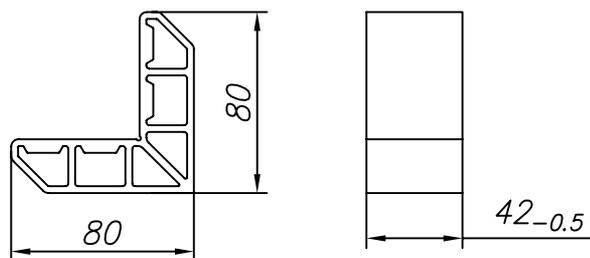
Изготовление соединителя углового FLGU.400.0914
